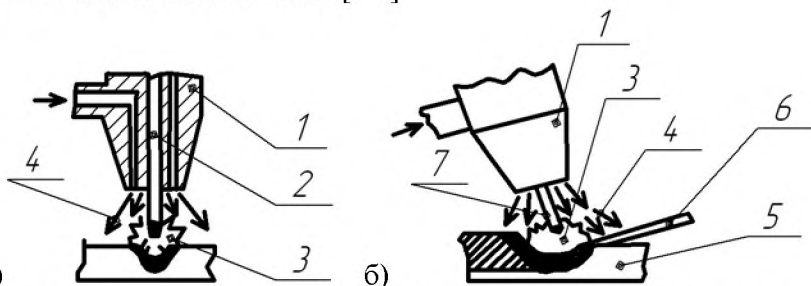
Схема наплавки плавящимся (а) и неплавящимся (б) электродами в среде защитных газов: 1 - газовое сопло; 2 - плавящийся электрод; 3 - дуга; 4 - защитный газ; 5 - деталь; 6 - присадочный пруток; 7 - неплавящийся электрод
